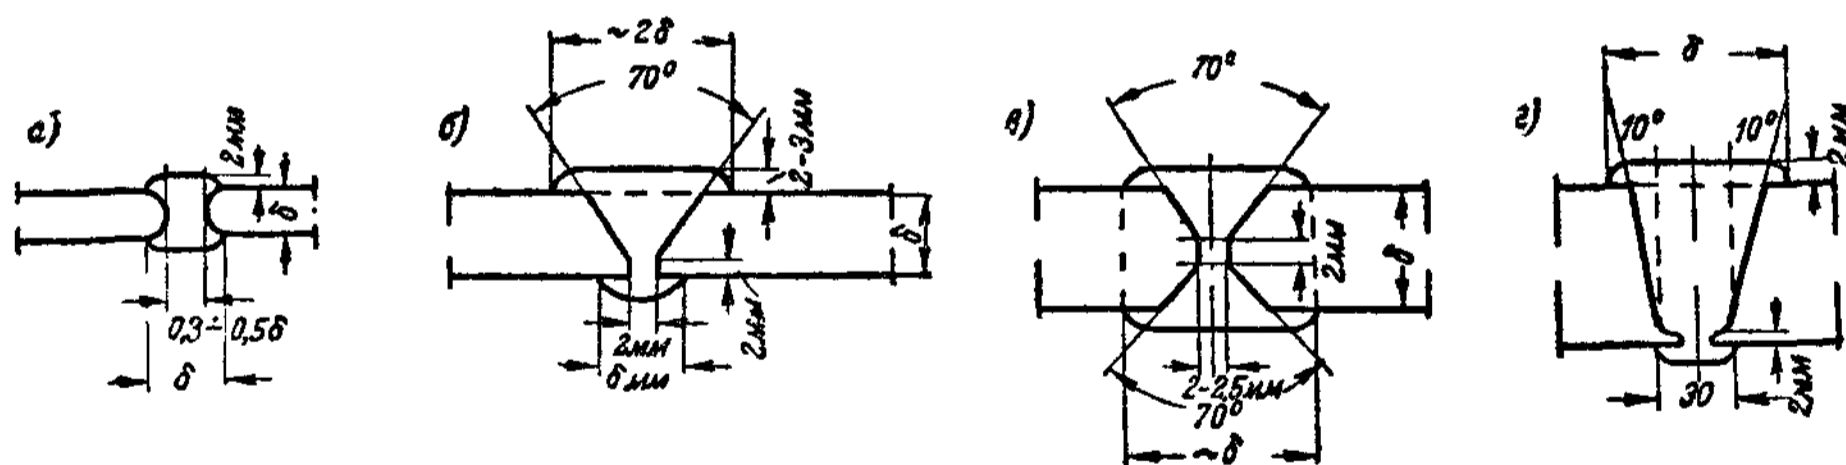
Разделка листов под стыковой шов при ручной сварке
